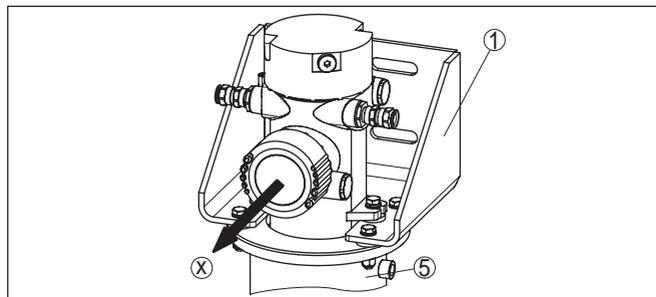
Montagerichtung des Sensors zum Befestigungswinkel
